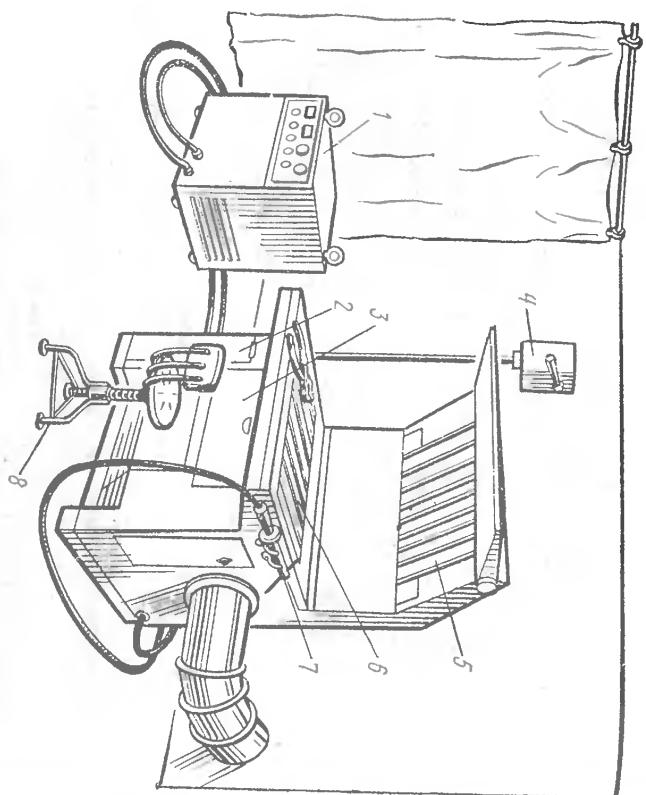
Стационарный сварочный пост ручной дуговой сварки:
